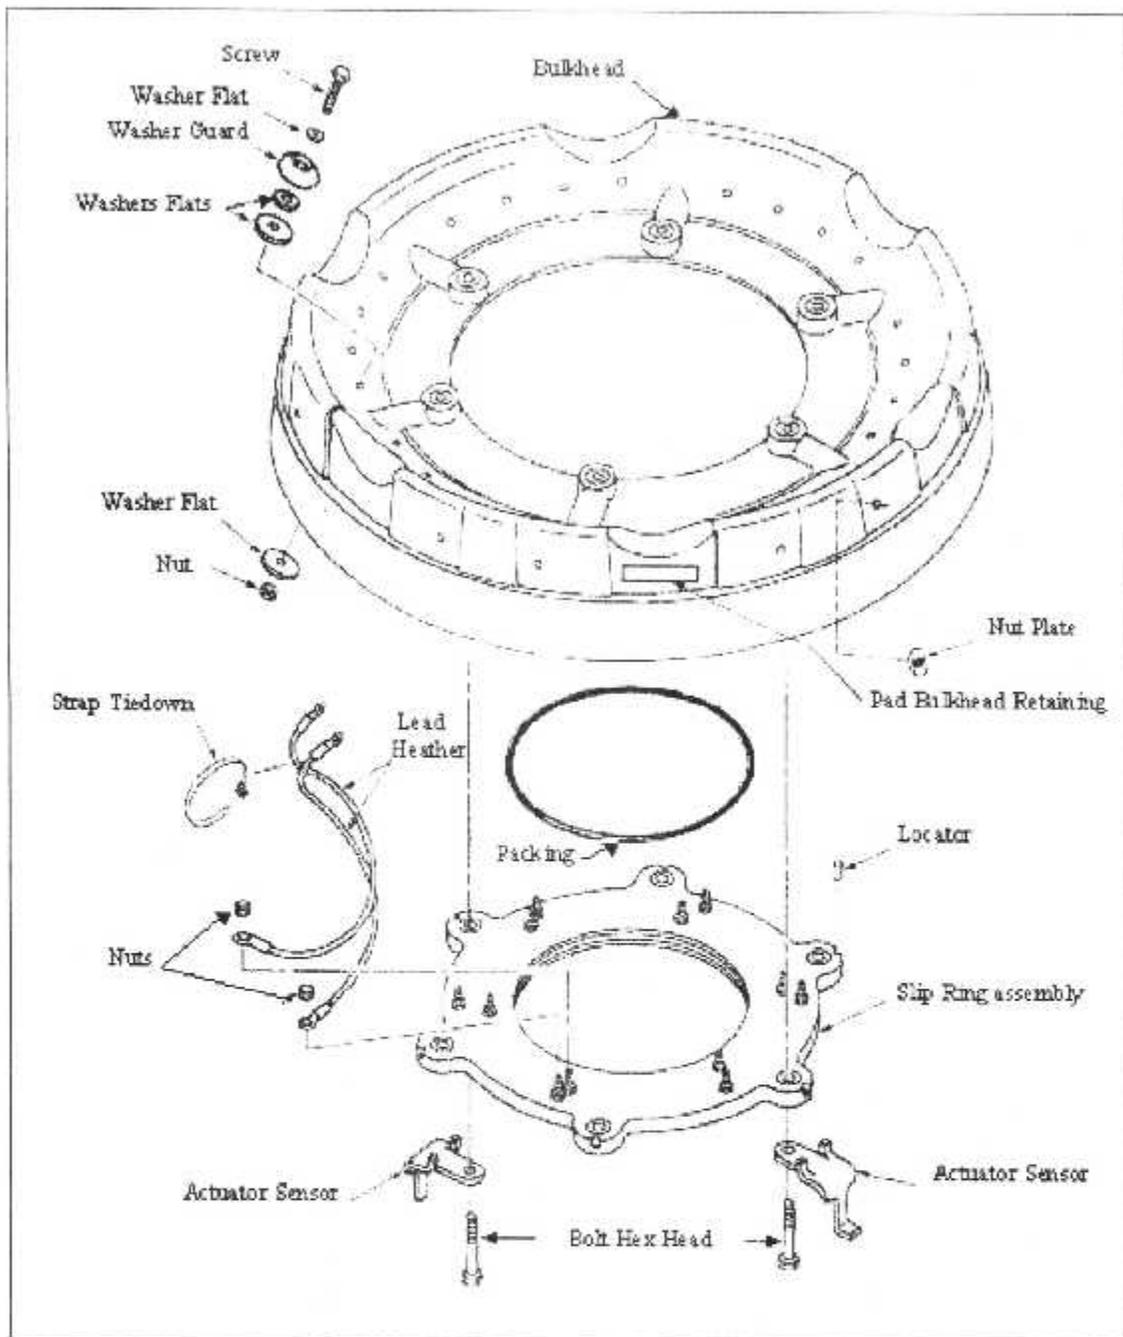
Installation de la cloison étanche et le collecteur de dégivrage.
